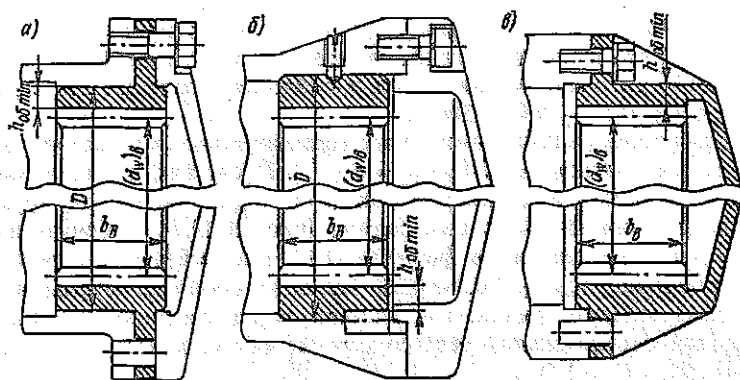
Неплавающие невращающиеся центральные зубчатые колеса с внутренними зубьями
